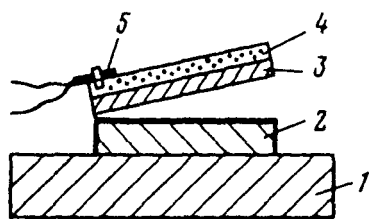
Установка для сварки металла взрывом:
